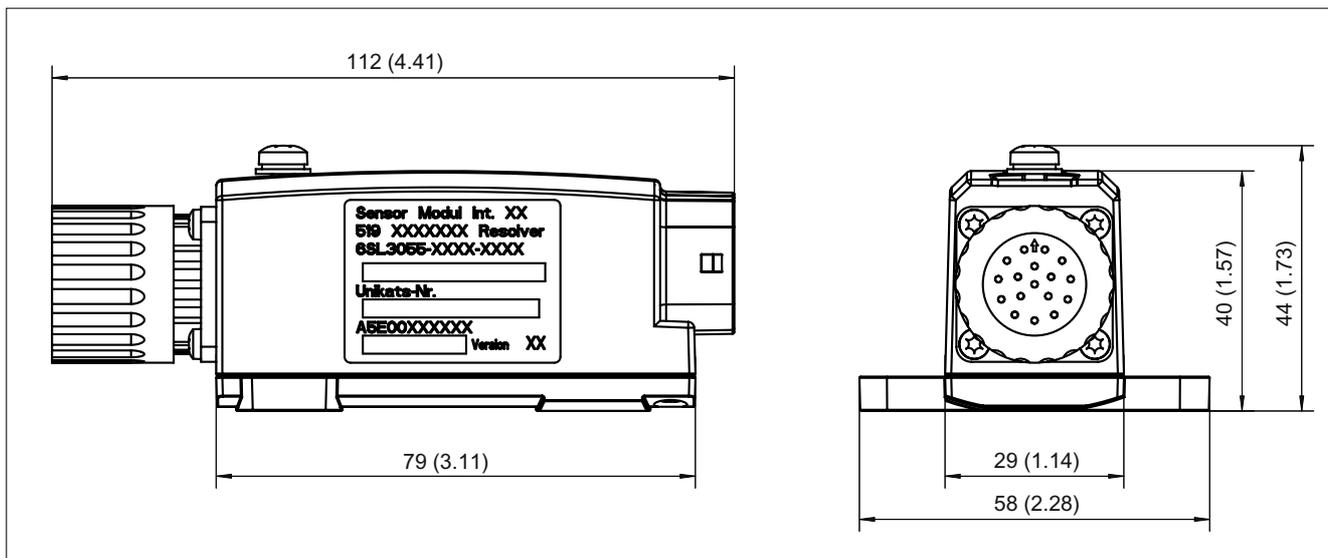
Disegno quotato Sensor Module External SME25, tutte le misure in mm e (inch),
